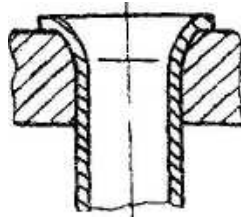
Крепление труб в трубной решетке развальцовкой с отбортовкой
